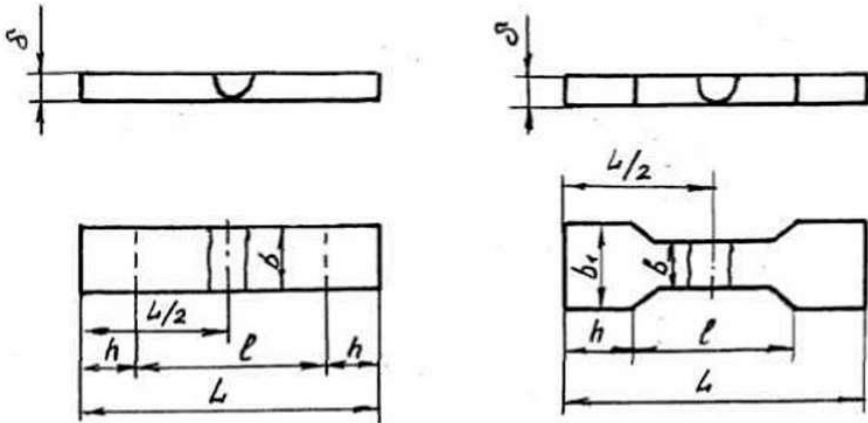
Схема зразків для випробування зварного з'єднання на статичний розтяг
